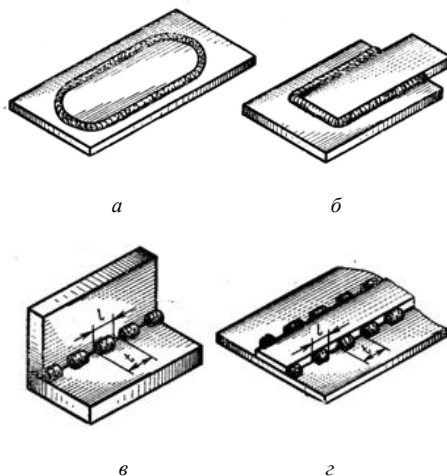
Сварные швы: а – сплошной замкнутый; б – сплошной разомкнутый; в – прерывистый цепной; з – с шахматным расположением участков
